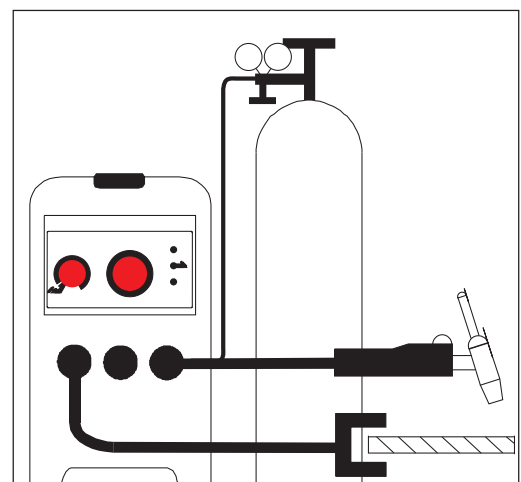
TP 2000 équipé pour le soudage TIG
